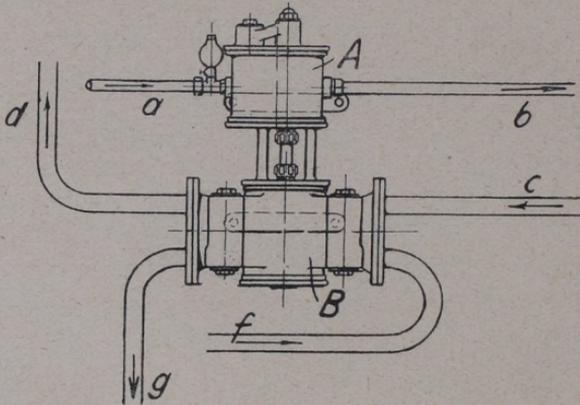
Speisewasserpumpe Bauart „Caille“.
